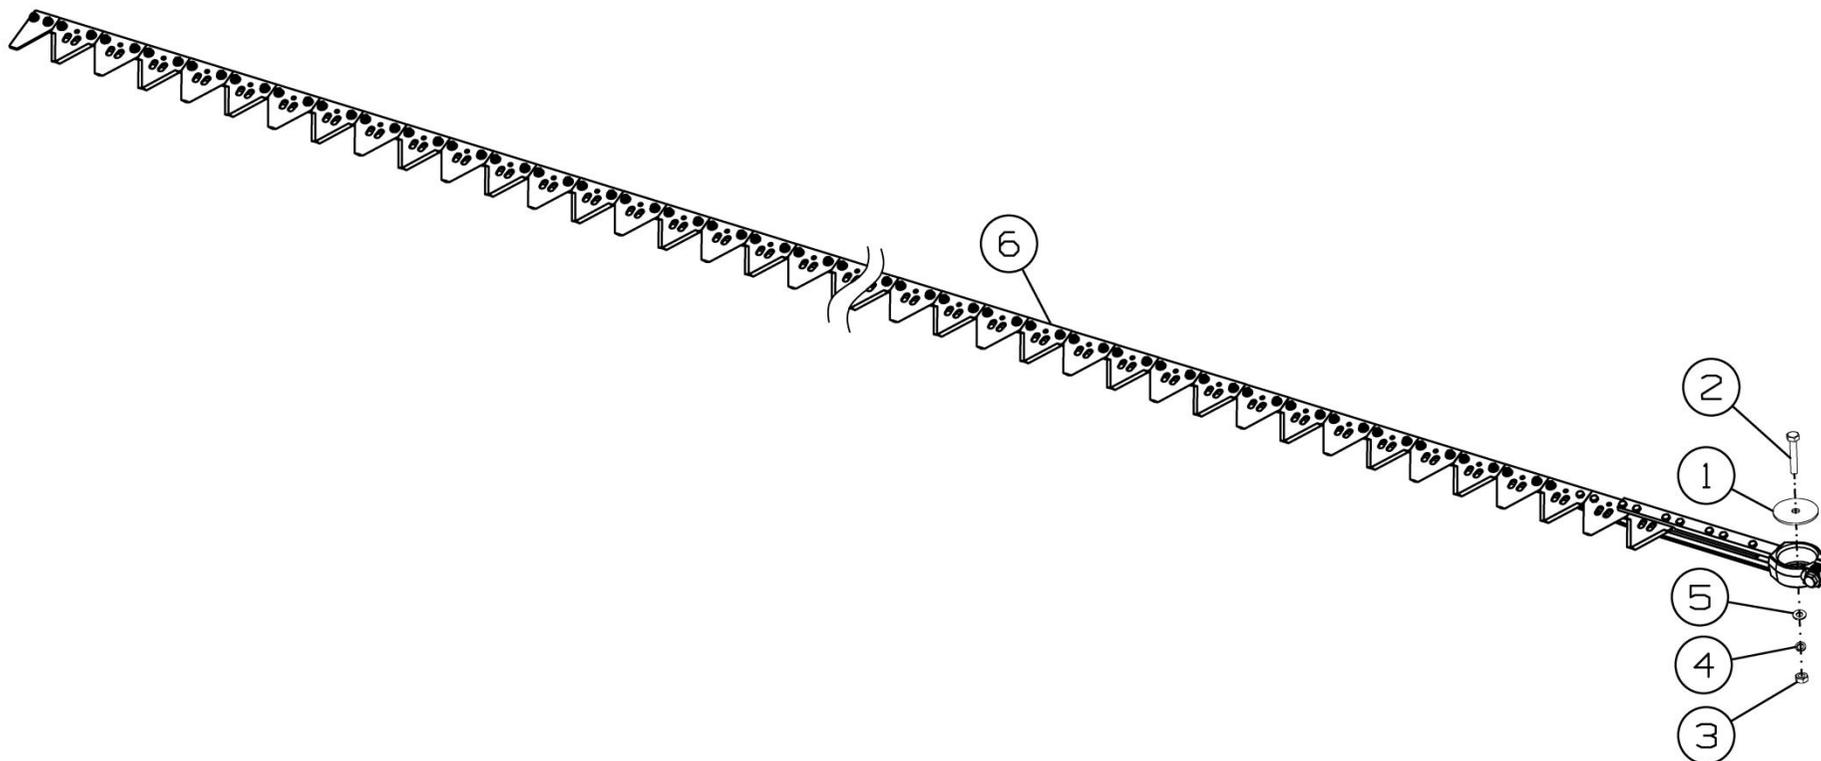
Установка запасного ножа SS-780.12.00.020
